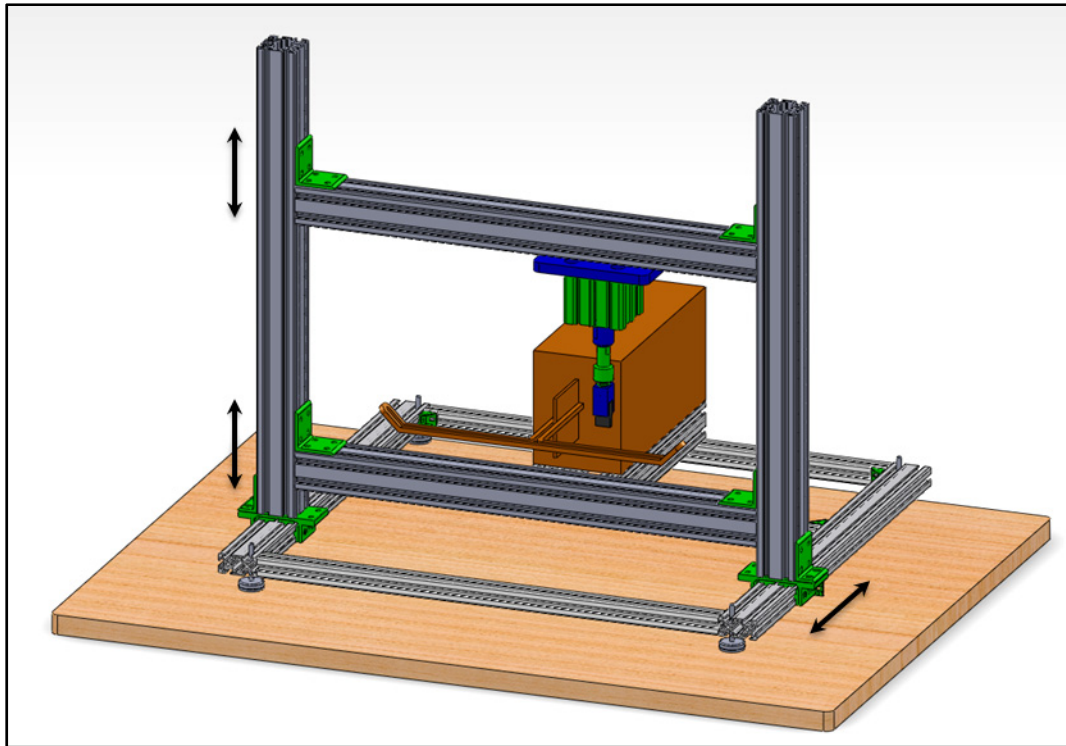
Montage de soudage par induction : vue 3D de la structure et les mouvements possibles
